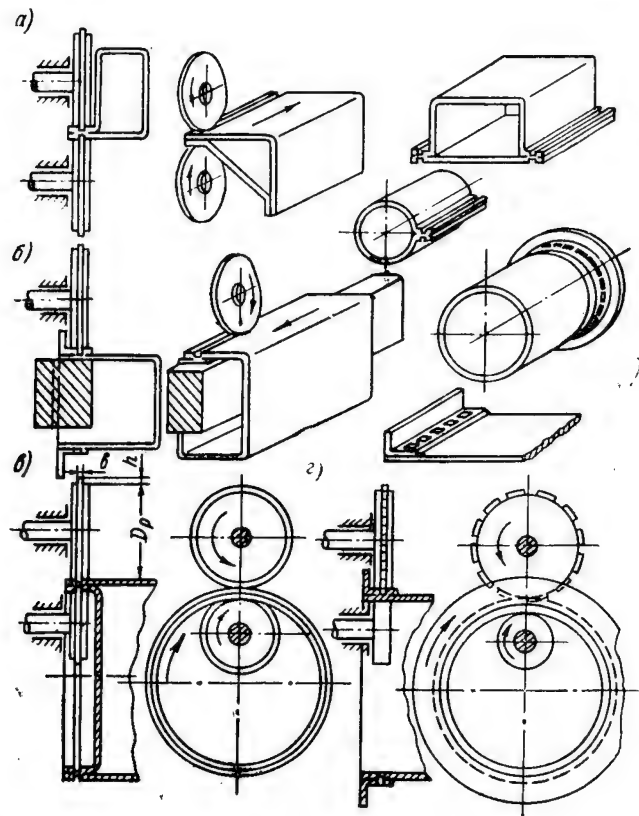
Схемы различных способов шовной роликовой сварки давлением и примеры соединений
